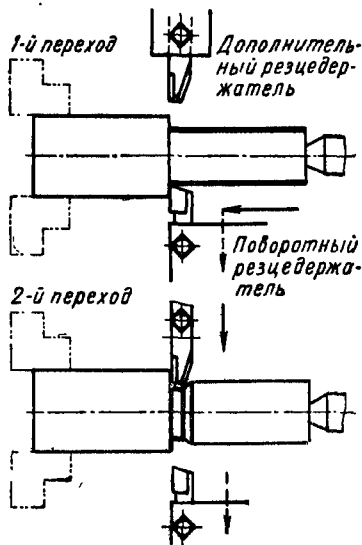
Обработка ступенчатого валика с помощью дополнительного заднего резцедержателя.
